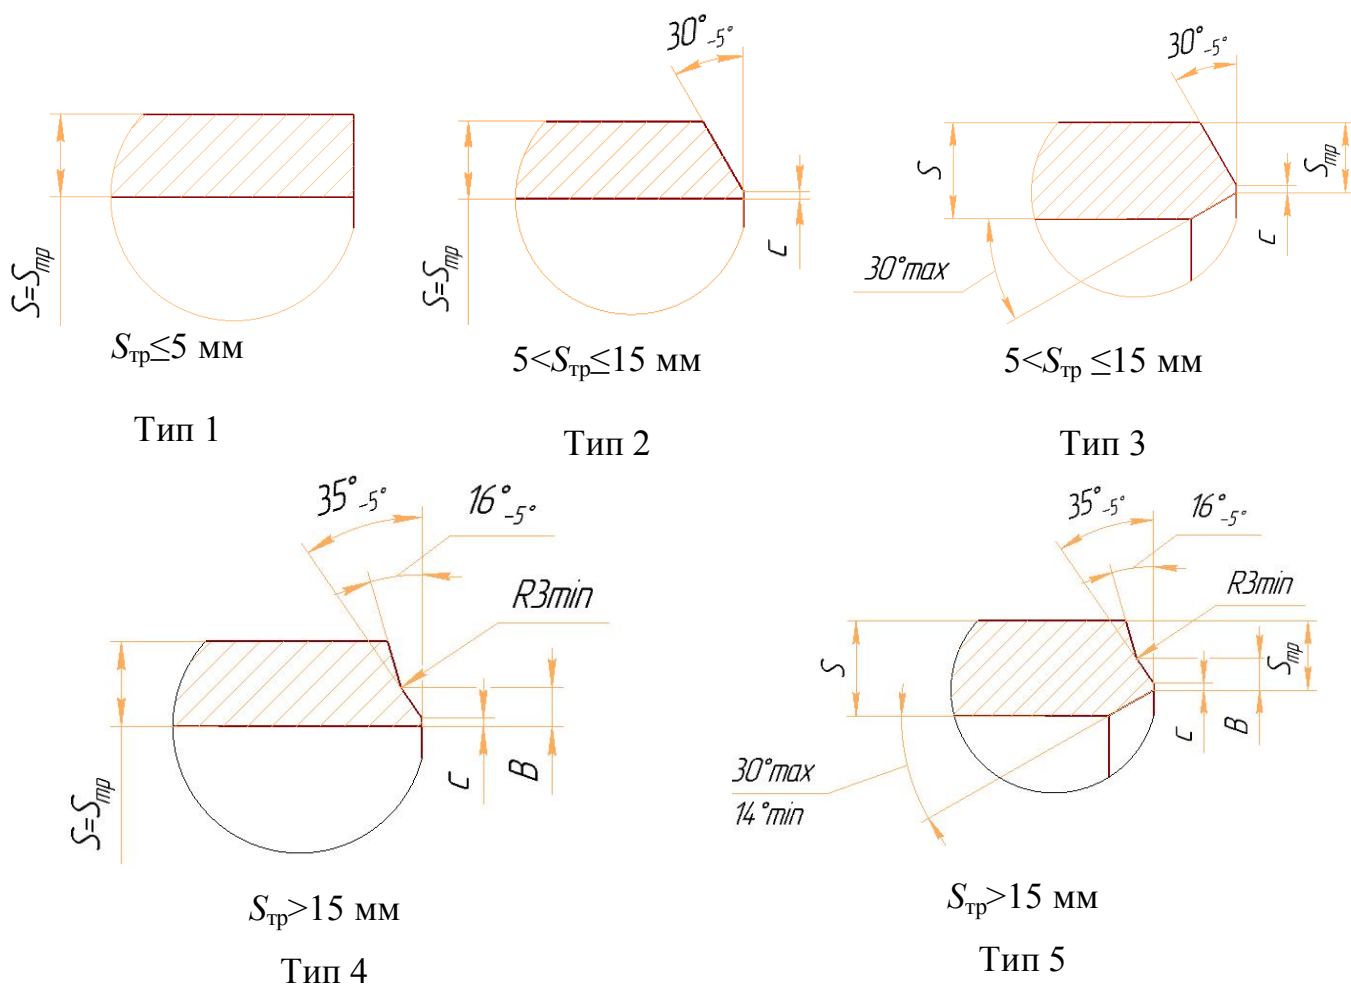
Типы обработки кромок торцов отводов под сварку
